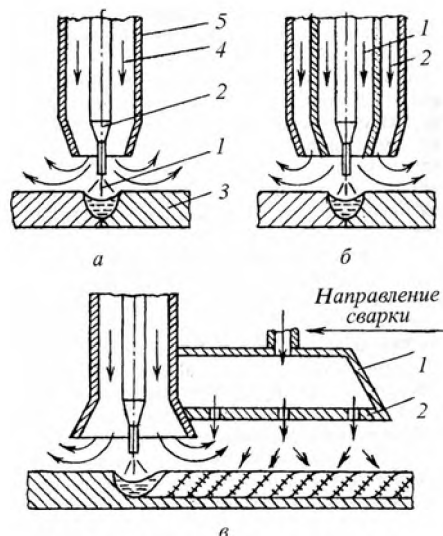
Схема дуговой сварки в среде защитных газов
